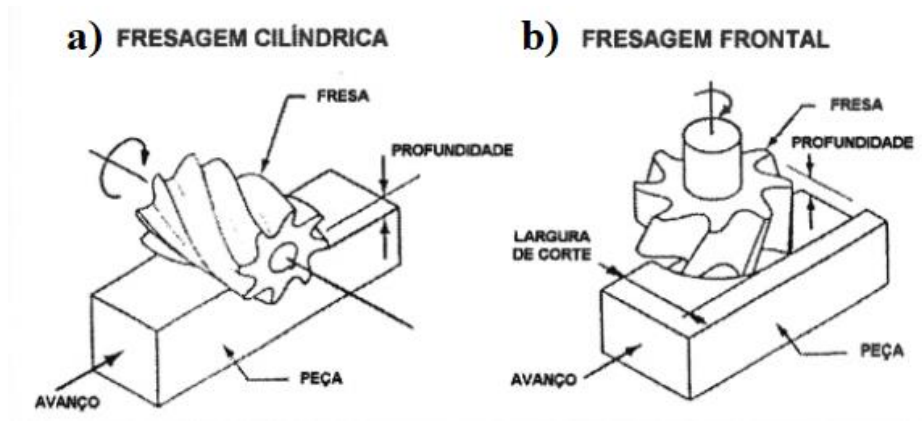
Fresagem cilíndrica (a) e fresagem frontal (b), adaptada de [21].
